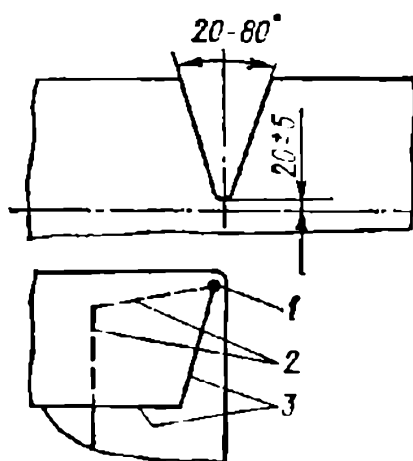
Выкройка и сварка швов на трехгранных углах пластиковой футеровки:
